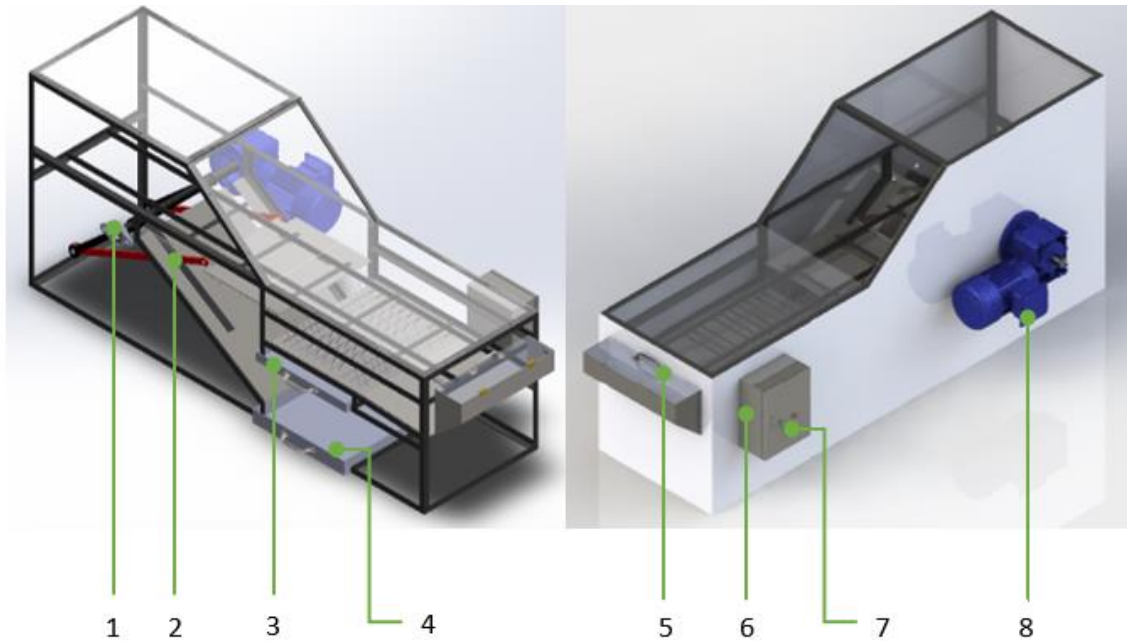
Estructura y armazón de la máquina escarmenadora.
